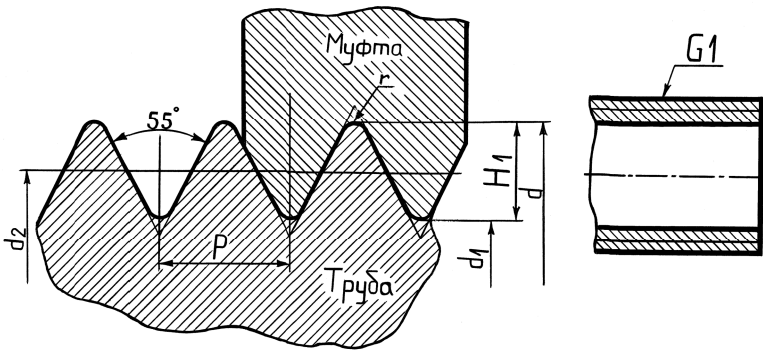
Позначення трубної циліндричної різьби на кресленнях
